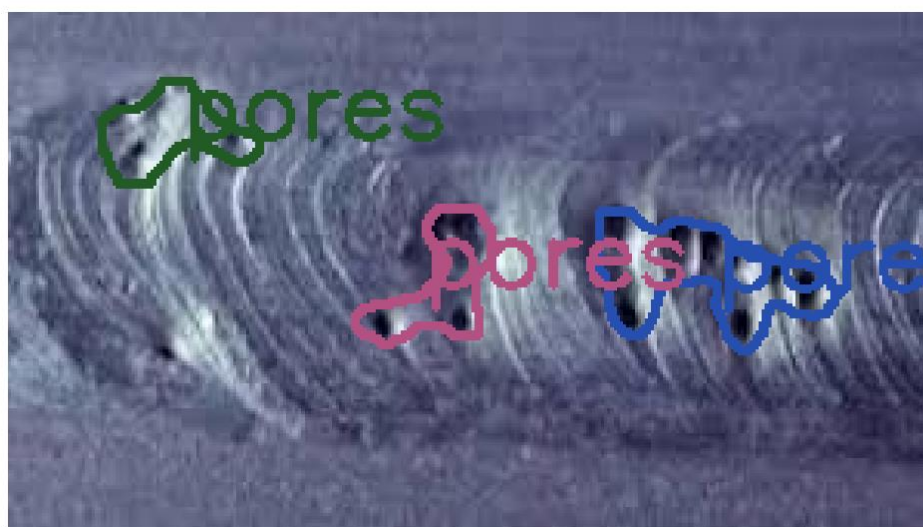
Пример распознанного сварного шва с дефектами
